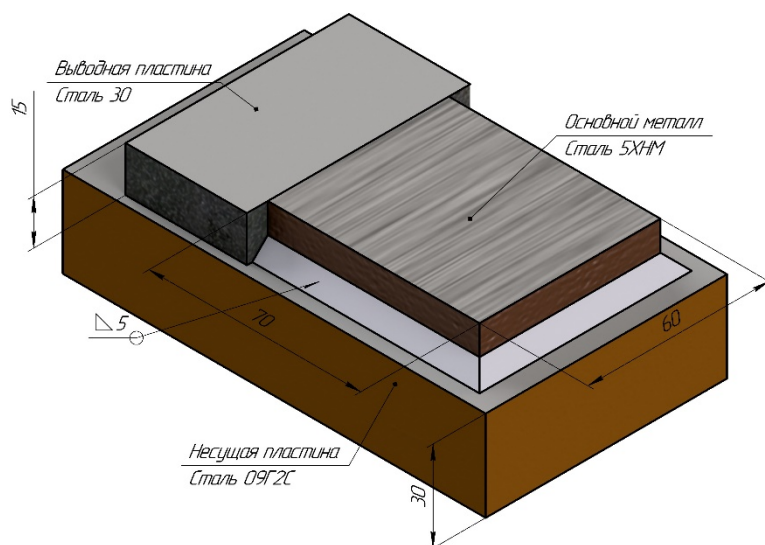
Схема монтажа пластины ОМ перед наплавкой
